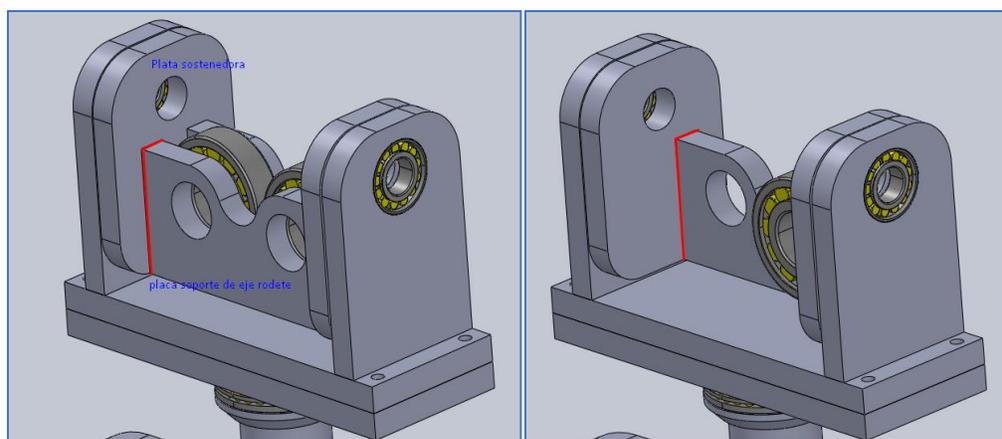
Ubicación de cordón de soldadura entre la placa soporte de rodamiento y placa sostenedora. Fuente: Elaboración propia.
